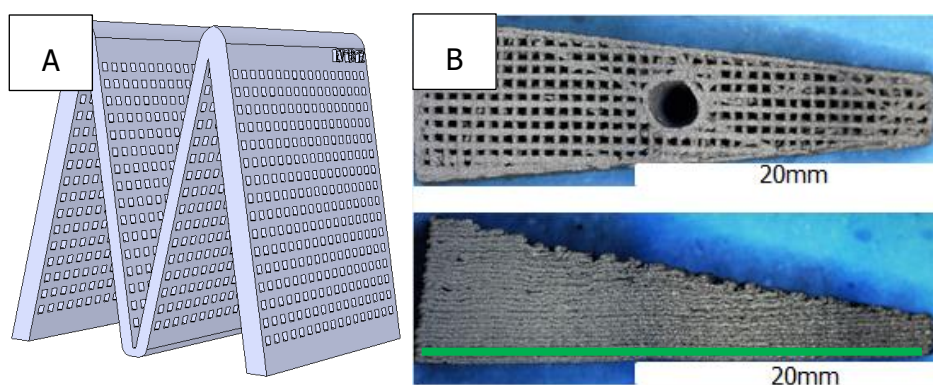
A) Diseño en 3D de un molde para colocar la muestra durante la inmersión en agua y B) muestra tras la inmersión con el uso del molde.
